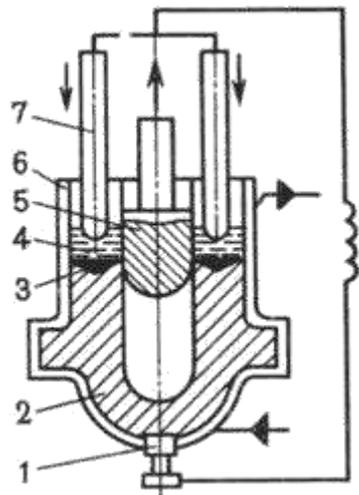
Схема изготовления отливок электрошлаковым литьем
